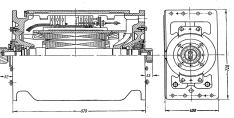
Габаритные размеры электродвигателя типа МАД 191/11 м
